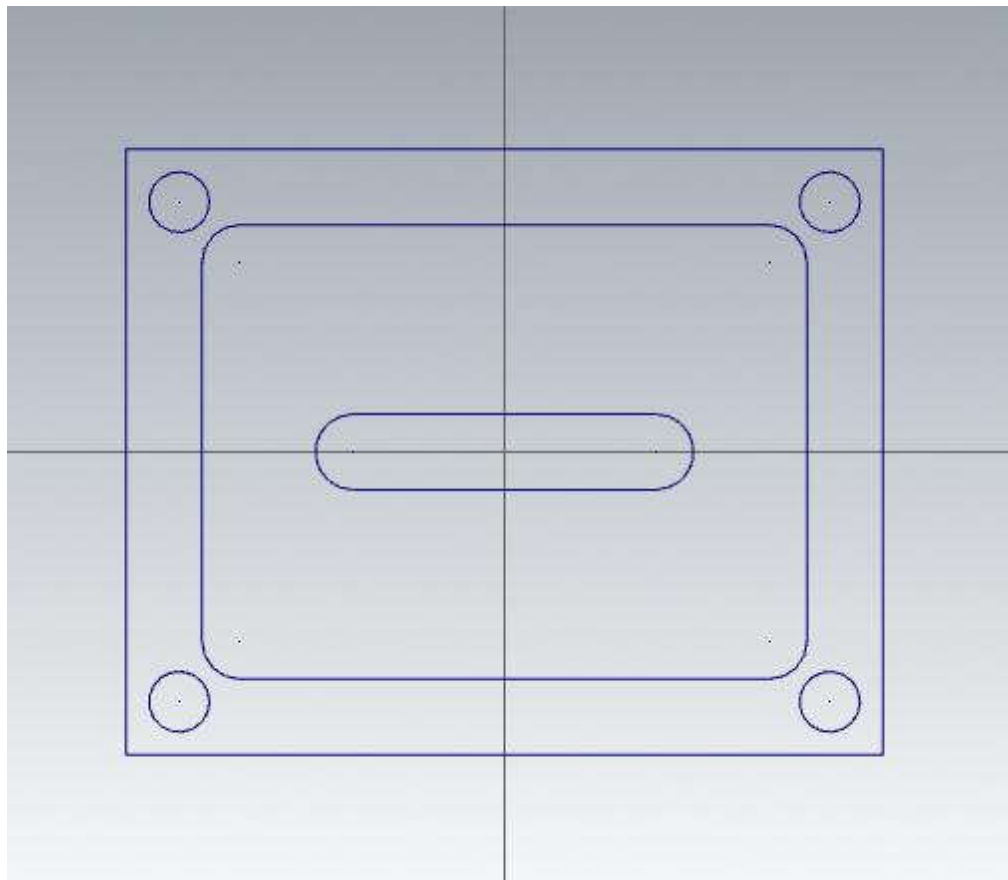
Vue de dessus de la pièce prismatique en 2D
